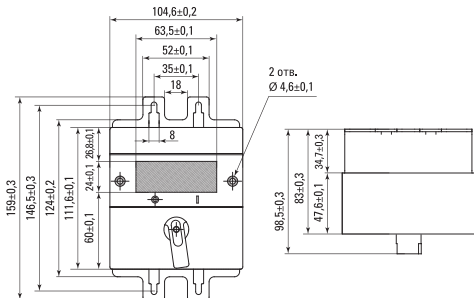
Габаритные размеры моторного привода к ВА-99М 250
